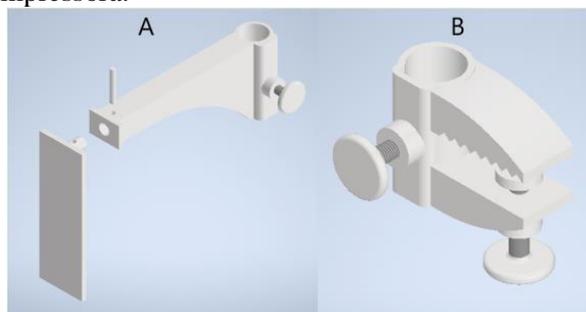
Parte A - estrutura para a fixação do tracionador e Parte B -estrutura para fixação na carcaça.
